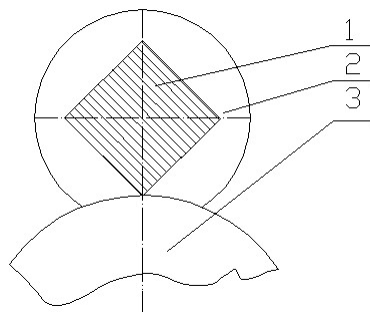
Схема ориентации распиливаемого образца относительно режущего инструмента: 1 – обрабатываемая заготовка; 2 – ориентирующая оправка; 3 – распиловочный диск
